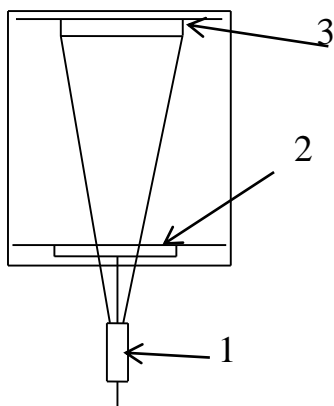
Схема съема оксидной пленки с поверхности неподвижной изложницы карусельной разливочной машины
